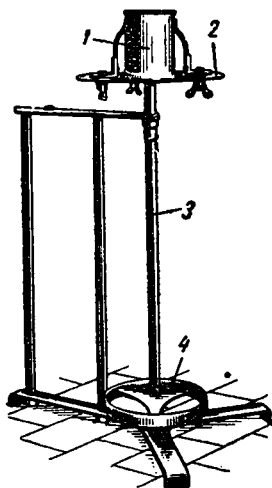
Передвижное приспособление для паяния днищ и ручек
